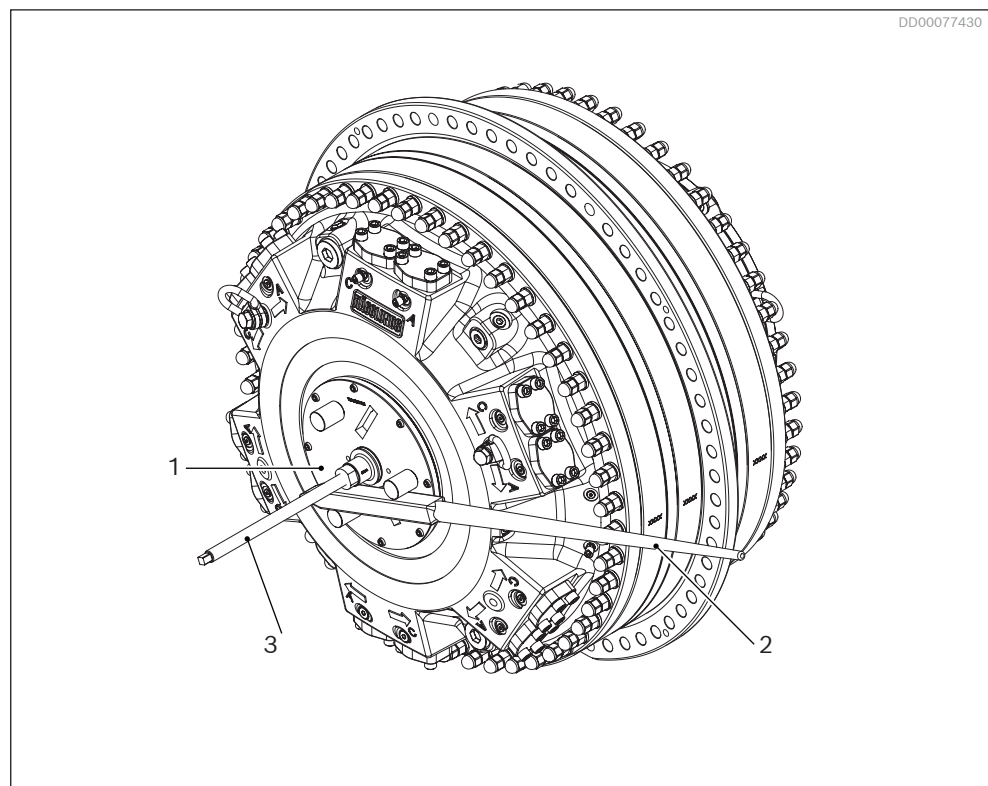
Инструмент для совмещения зубьев и пазов шлицевого соединения
